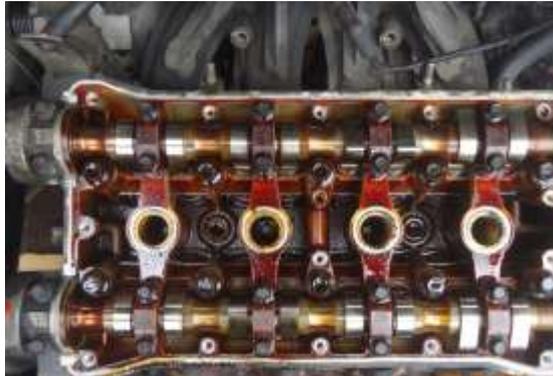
Desmontaje de Cubierta y Empaque Tapa Válvulas
